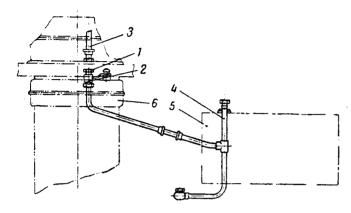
Схема для заливки разжижителя через дренажную трубку масляного бака:
